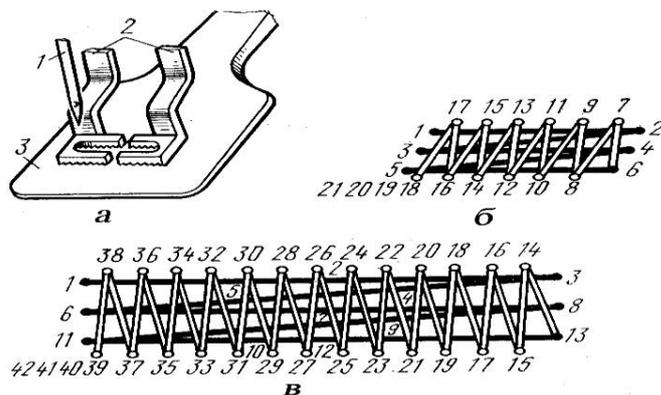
Процессы изготовления малой и большой закрепок на машине 220-М кл.
